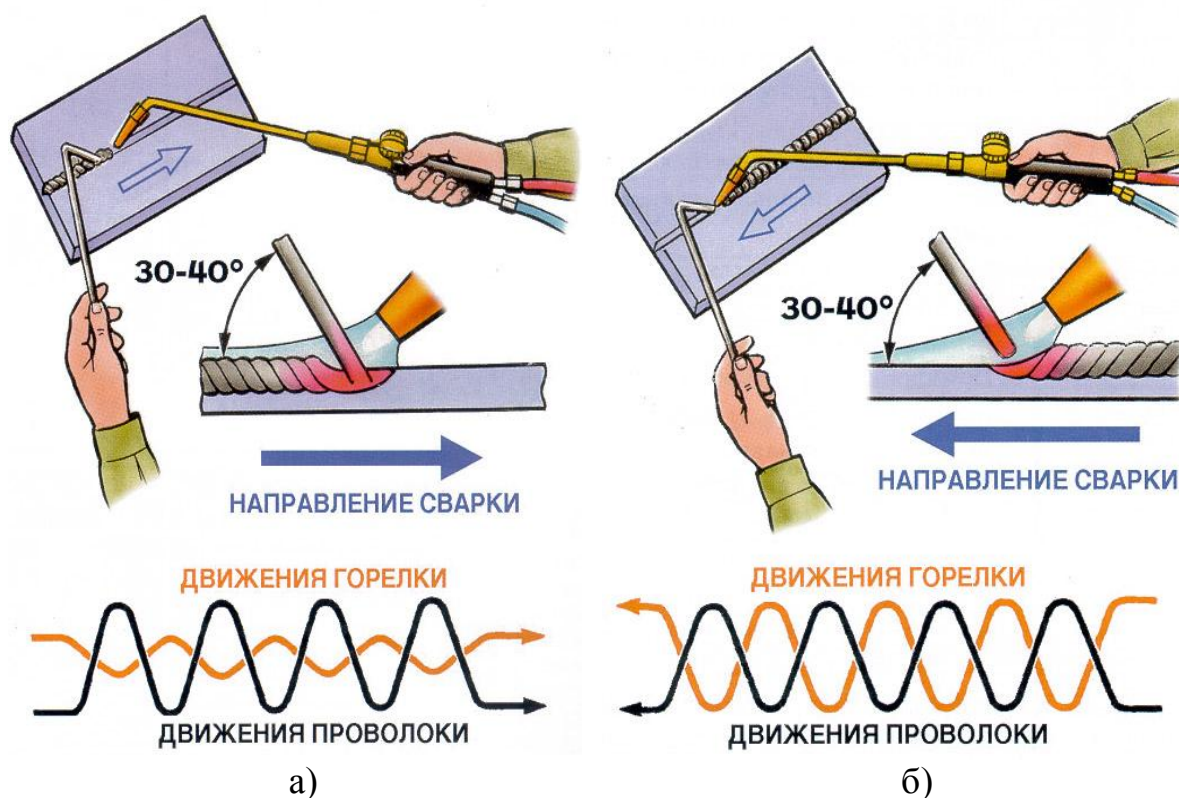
Способы газовой сварки: а – правый; б – левый
